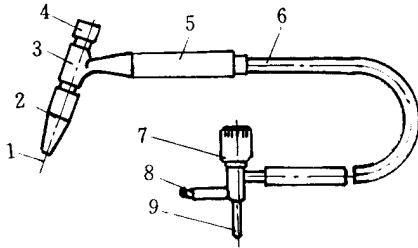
QQ—85/150—1 型气冷式 TIG 焊炬
